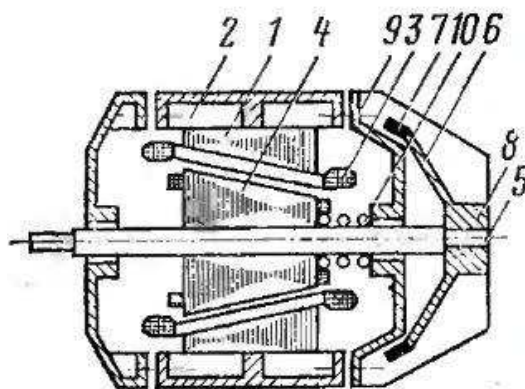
Схема конструкции самотормозящегося асинхронного электродвигателя с коническим скользящим ротором
